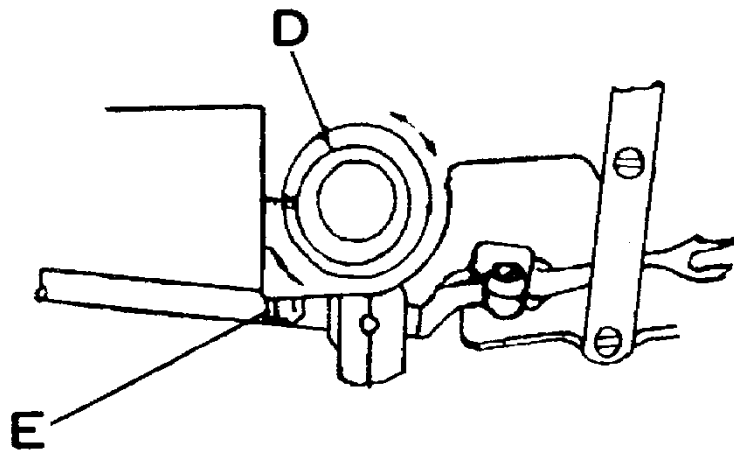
Регулировка положения вилочного петлителя относительно иглы
